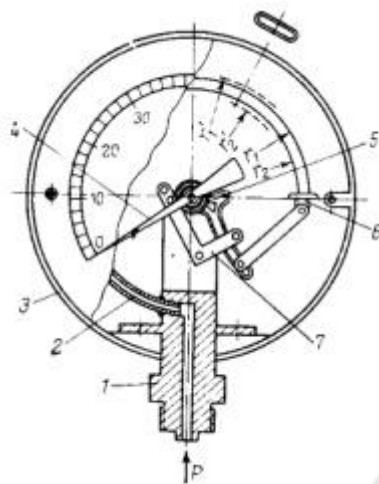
Схема манометра с одновитковой трубчатой пружиной
